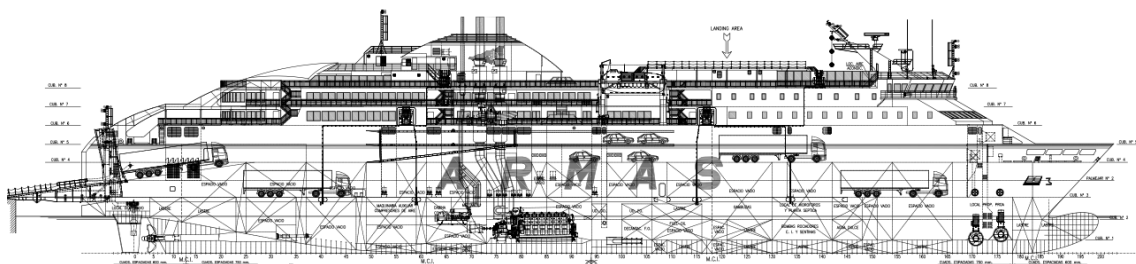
Disposición de las cubiertas. Fuente: Planos construcción Volcán de Tijarafe.
